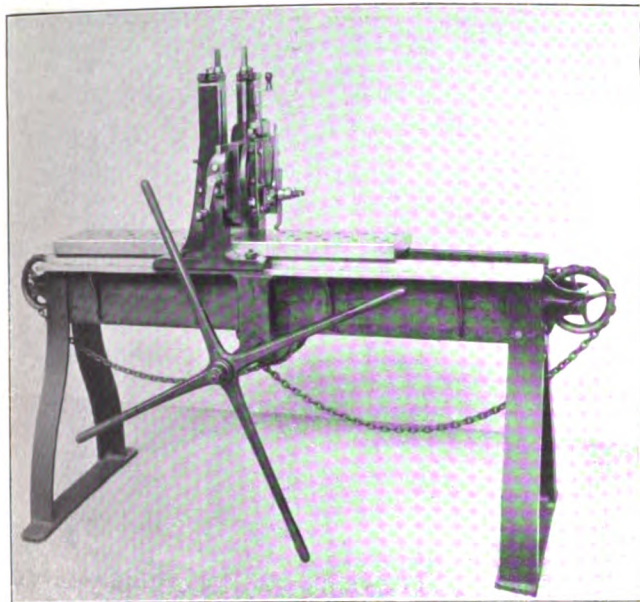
Stoßhobelmaschine (Shaping machine).
